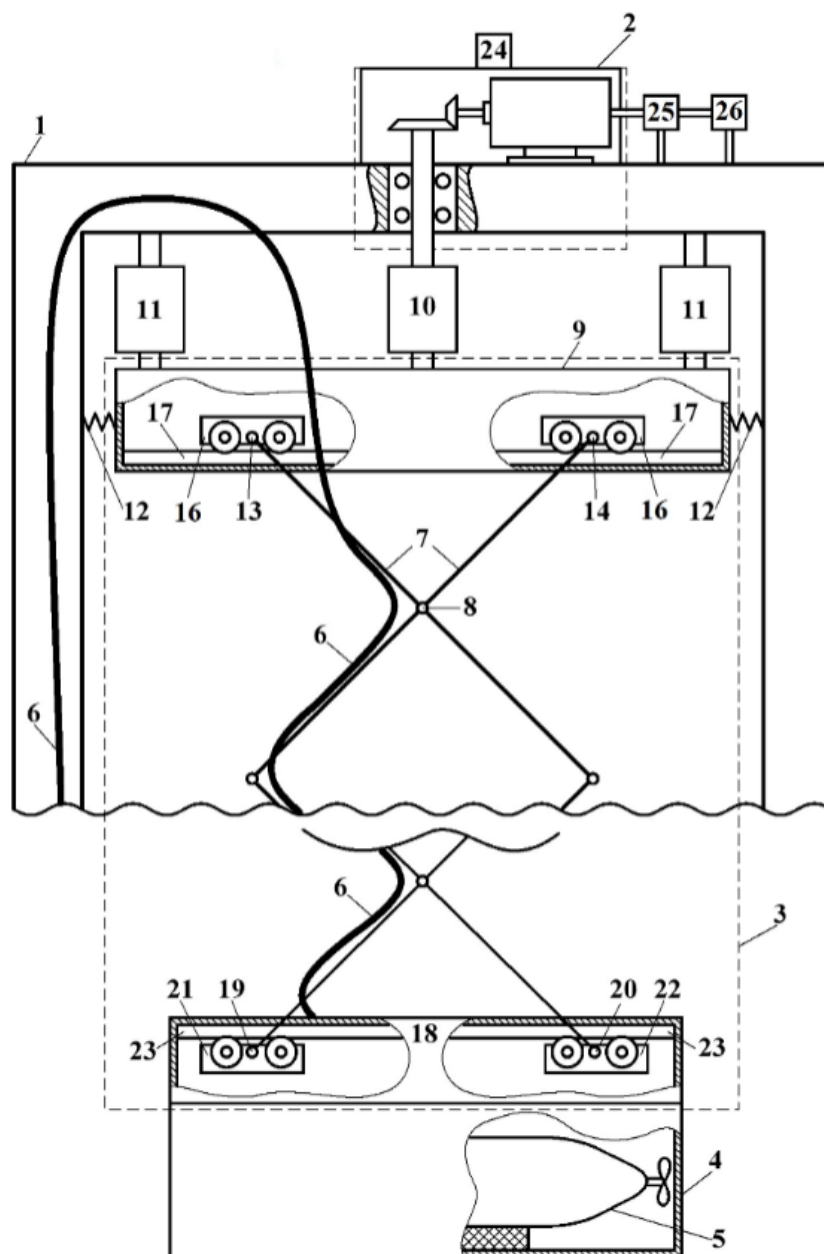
Фронтальный чертеж спускоподъемного устройства
